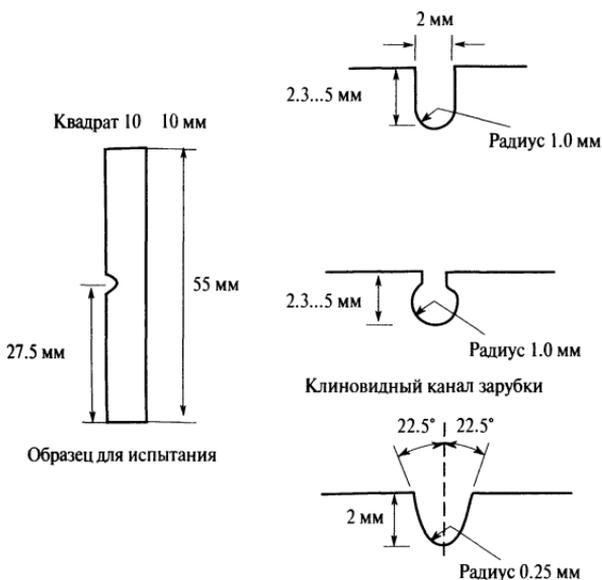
Стандартный металлический образец для испытания по Шарпи
